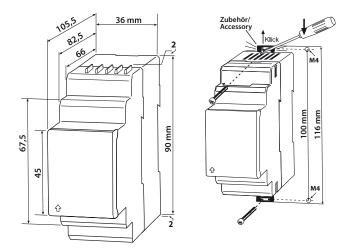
Maßbild, Skizze für Schraubbefestigung
